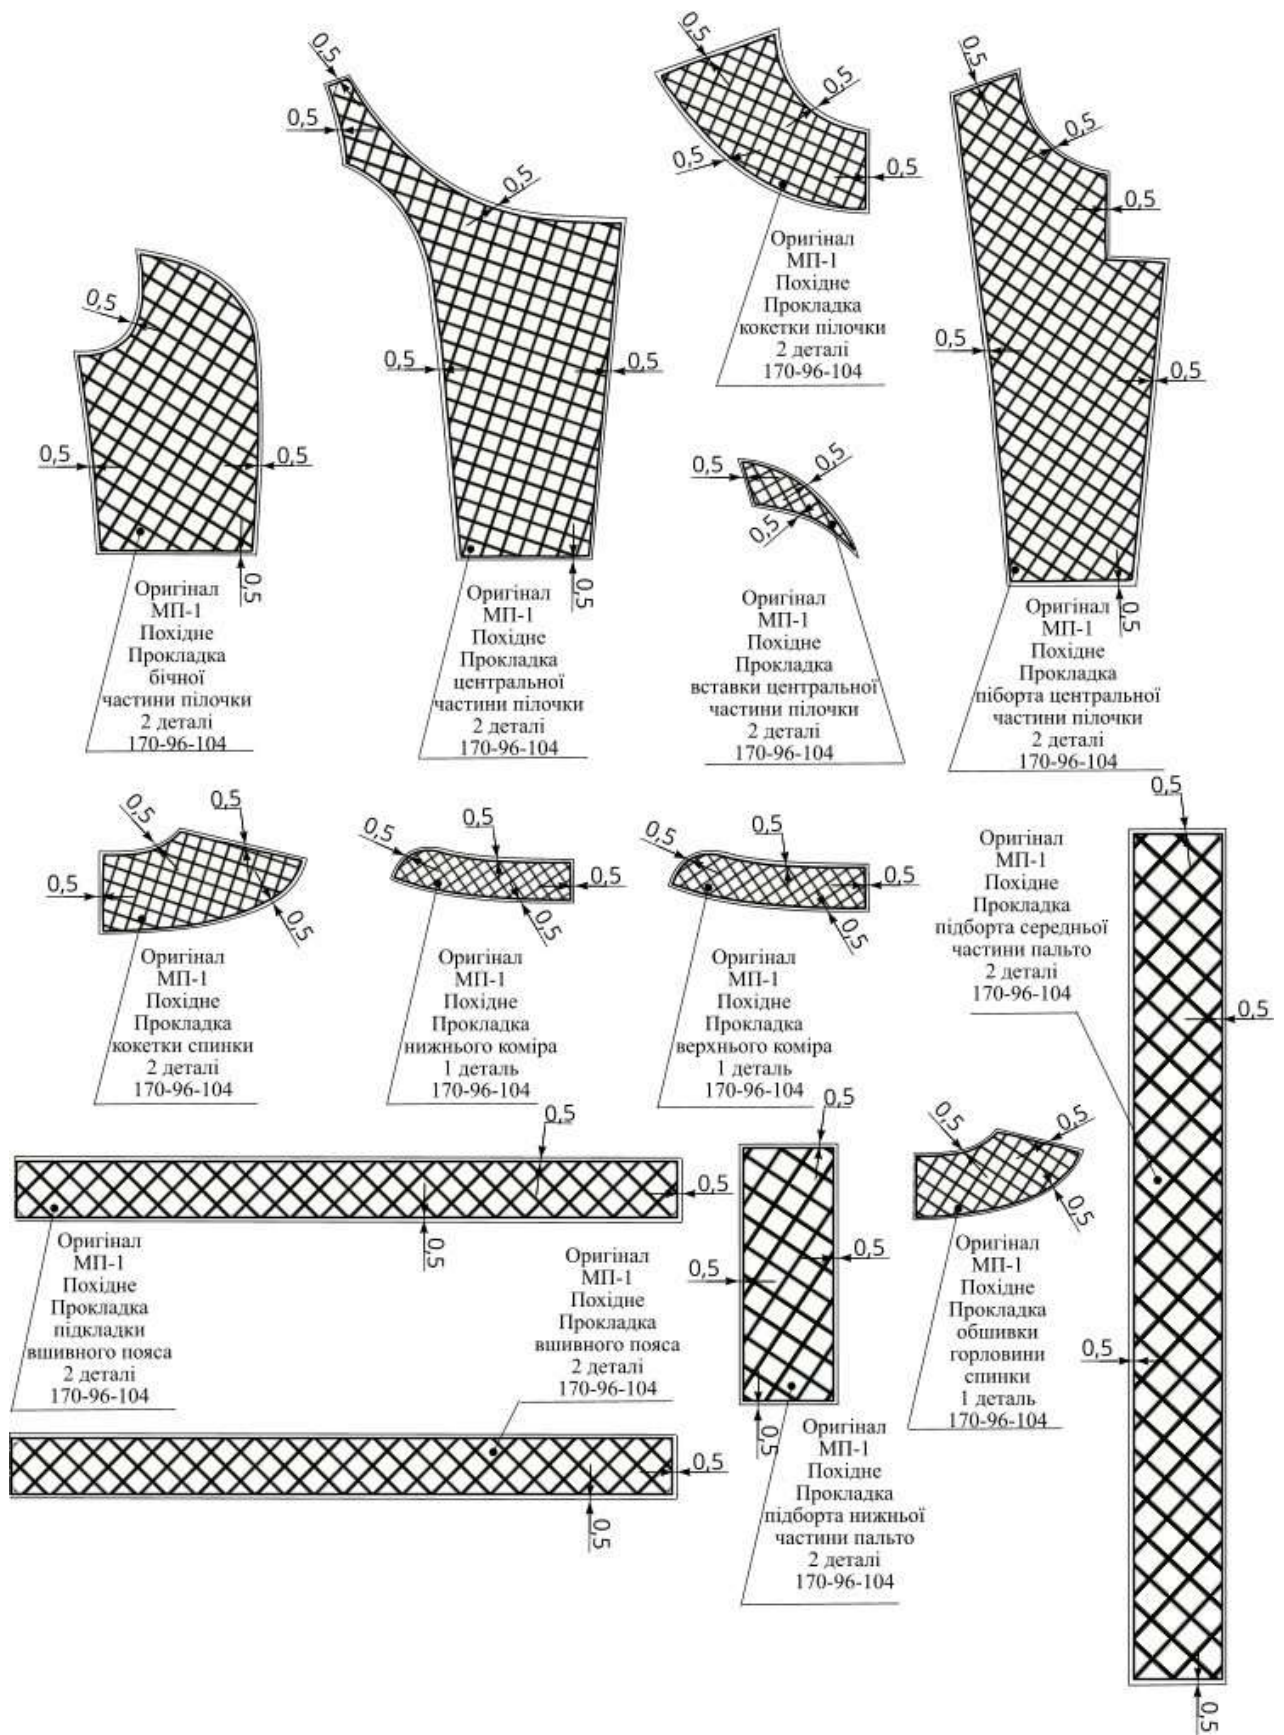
Схеми побудови лекал прокладки пальто жіночого (для фронтального дублювання)
